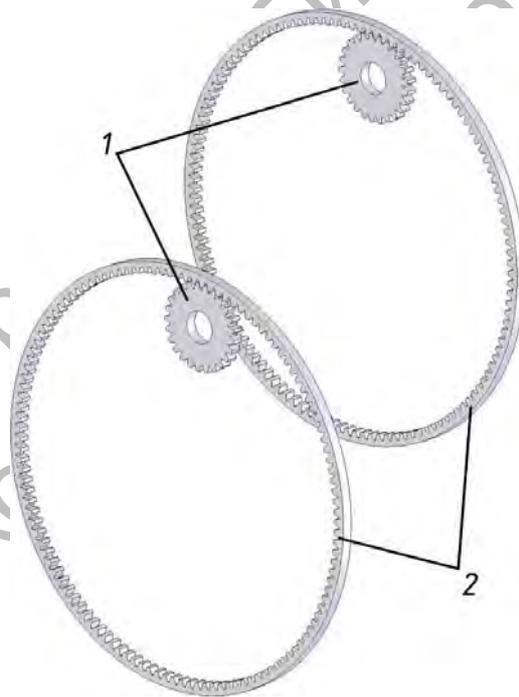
Общий вид компьютерной модели стандартной эвольвентной цилиндрической передачи с передаточным отношением 25: 1 – шестерня, 2 – колесо
